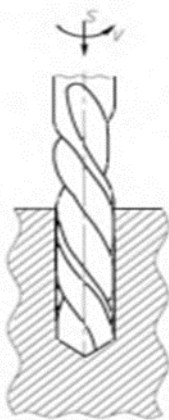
Схема процесу свердління на свердлильному верстаті
